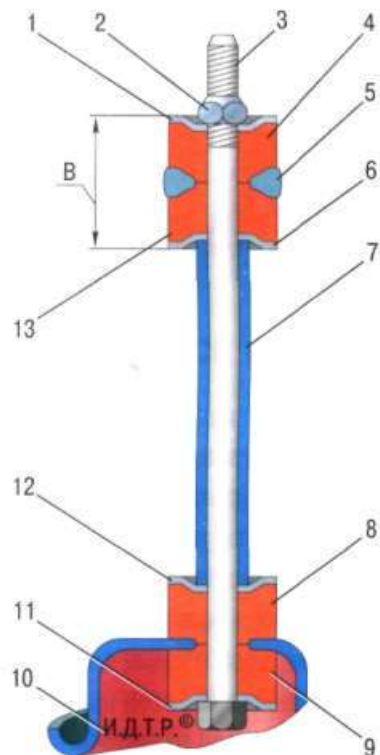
Стойка стабилизатора: 1, 6, 11, 12 – шайбы; 2 – гайка; 3 – болт; 4, 8, 9, 13 – резиновые втулки; 5 – штанга стабилизатора; 7 – распорная втулка; 10 – нижний рычаг; В – монтажный размер
